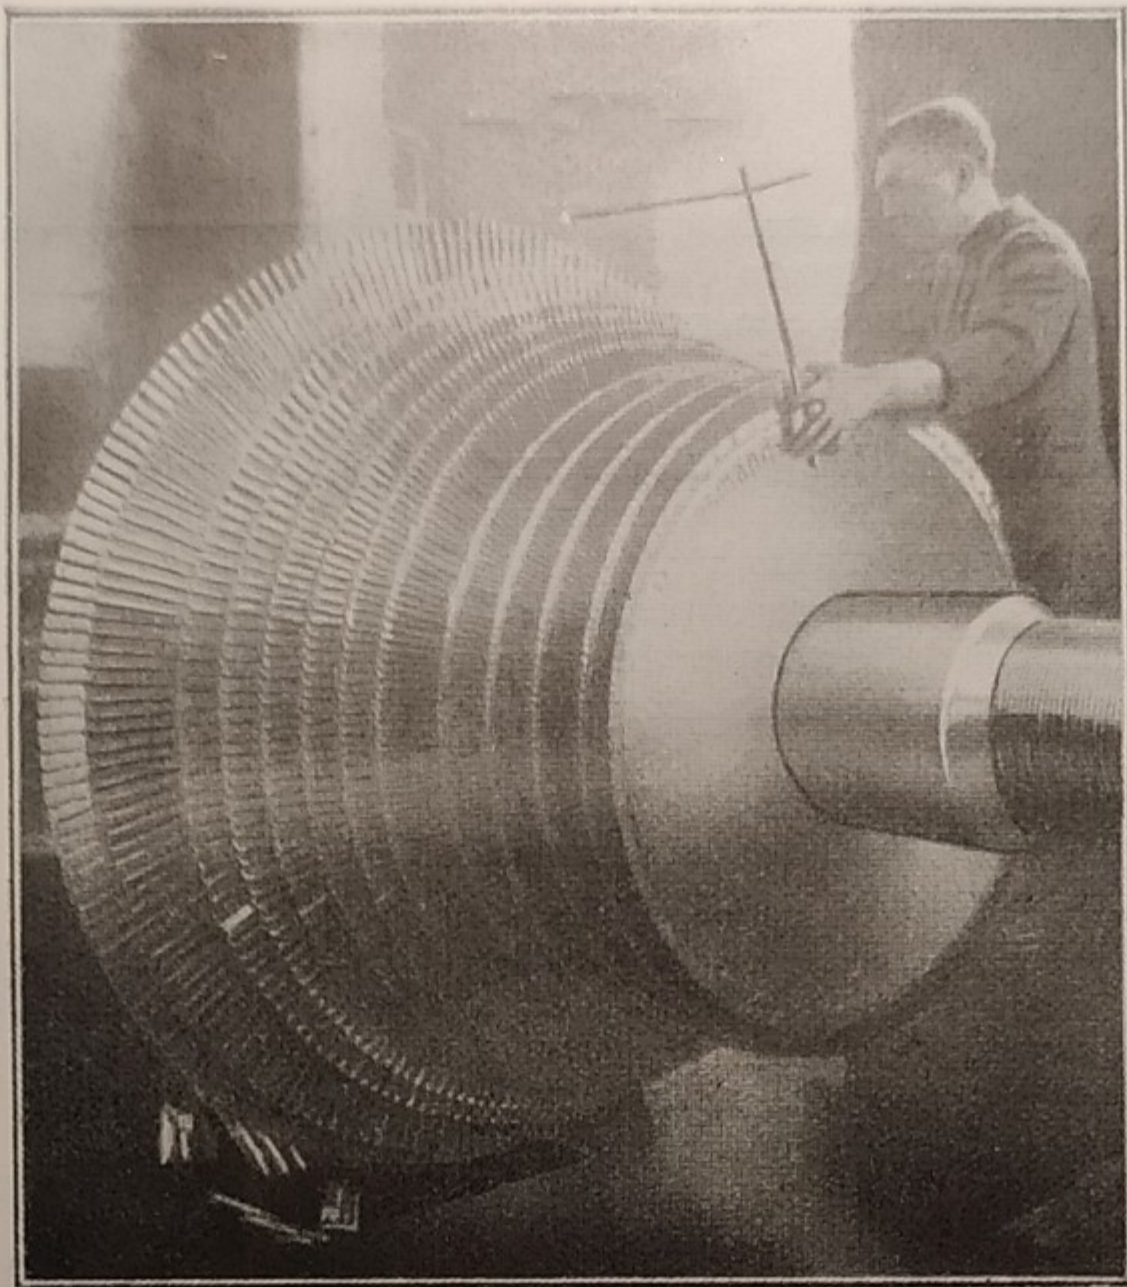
IL « ROTORE » DI UNA GROSSA TURBINA.
